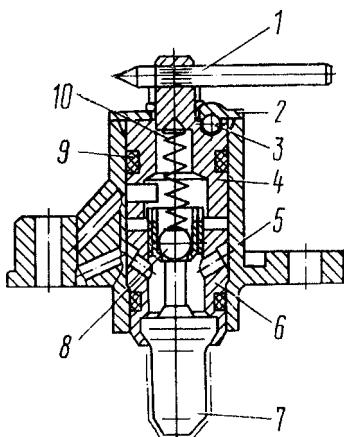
Включатель гидромуфты: 1 - рычаг пробки; 2 - крышка; 3, 8 - шарики; 4 - пробка; 5 - корпус включателя; 6 - клапан термосиловой (корпус); 7 - датчик термосиловой; 9 - кольцо уплотнительное; 10 - пружина
